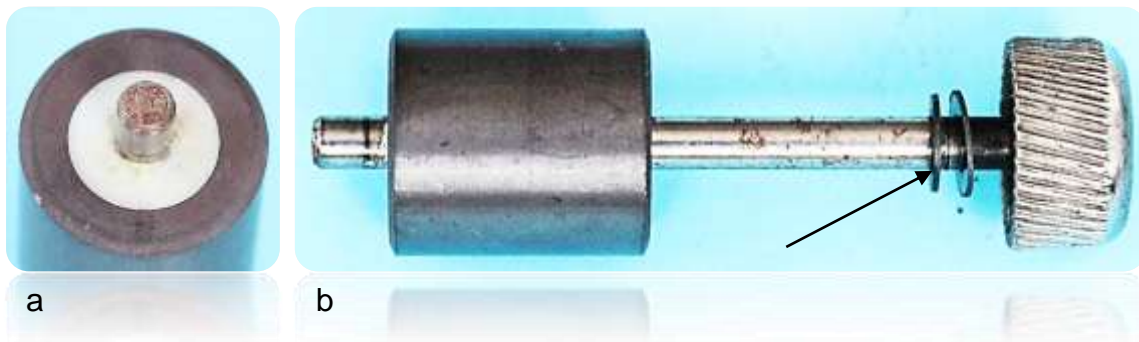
Achtpoliges Polrad (Durchmesser des Walzenmagneten 21 mm, axiale Länge 24 mm): a) Vergossene Welle, b) Polrad mit Welle, Reibrad und Sprengring zur Sicherung der axialen Position
